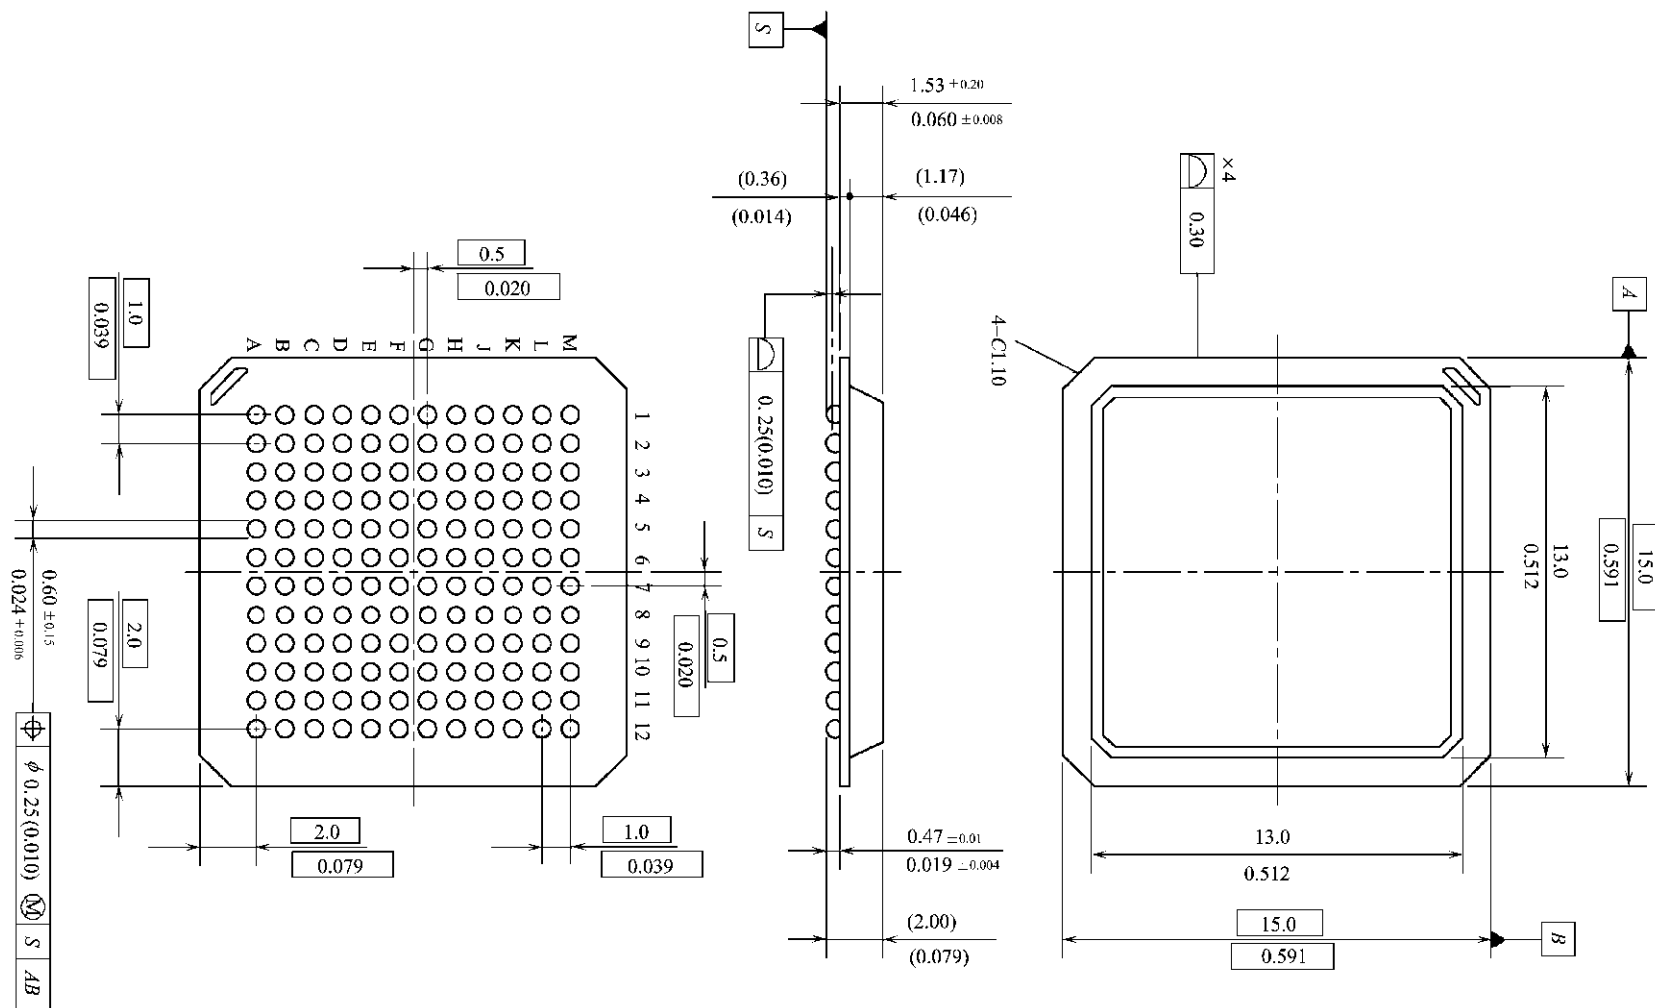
uN8031B 采用 BGA-144 封装尺寸
